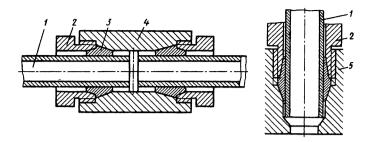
Безрезьбовое соединение труб: I — труба; 2 — зажимная втулка; 3 — уплотнитель; 4 — муфта; 5 — корпус узла трения
